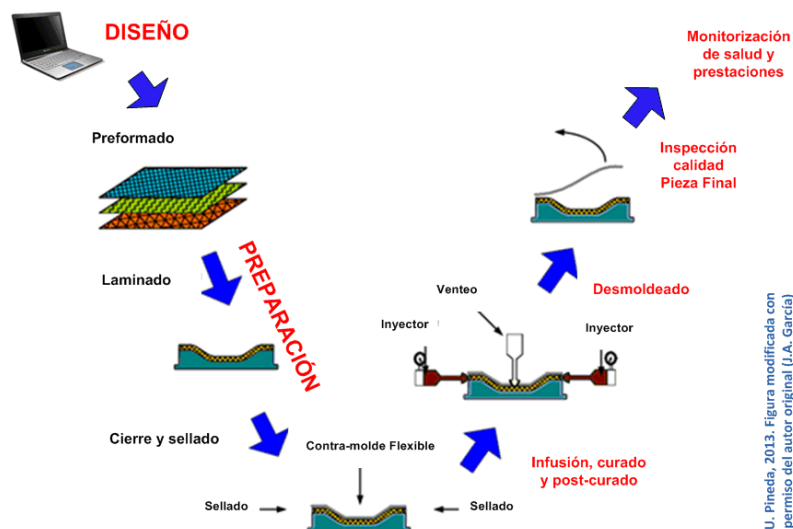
Proceso de fabricación mediante Moldeo por Infusión de Resina.
